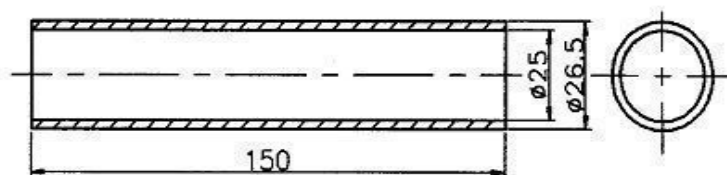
Эскиз обрабатываемой трубы из нержавеющей стали
